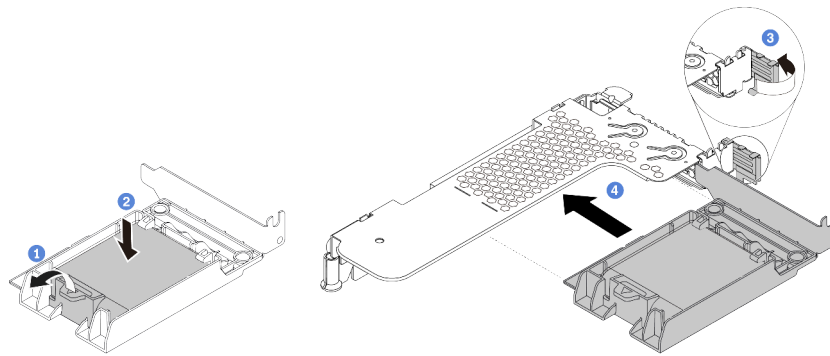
Installation du module d'alimentation flash RAID sur la carte mezzanine
